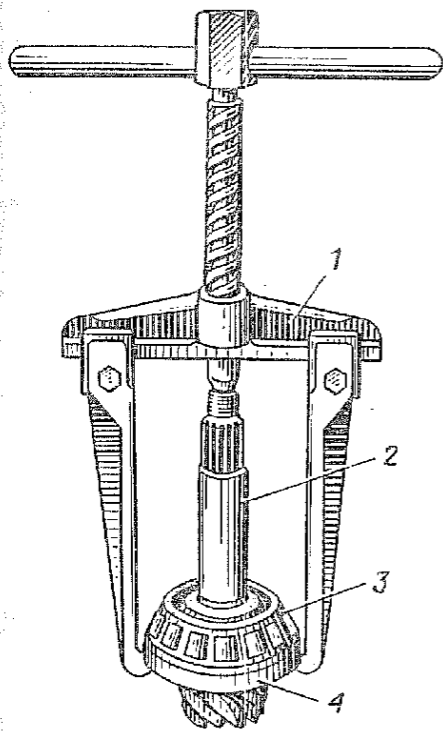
Спрессовка внутреннего кольца подшипника ведущей шестерни главной передачи:
